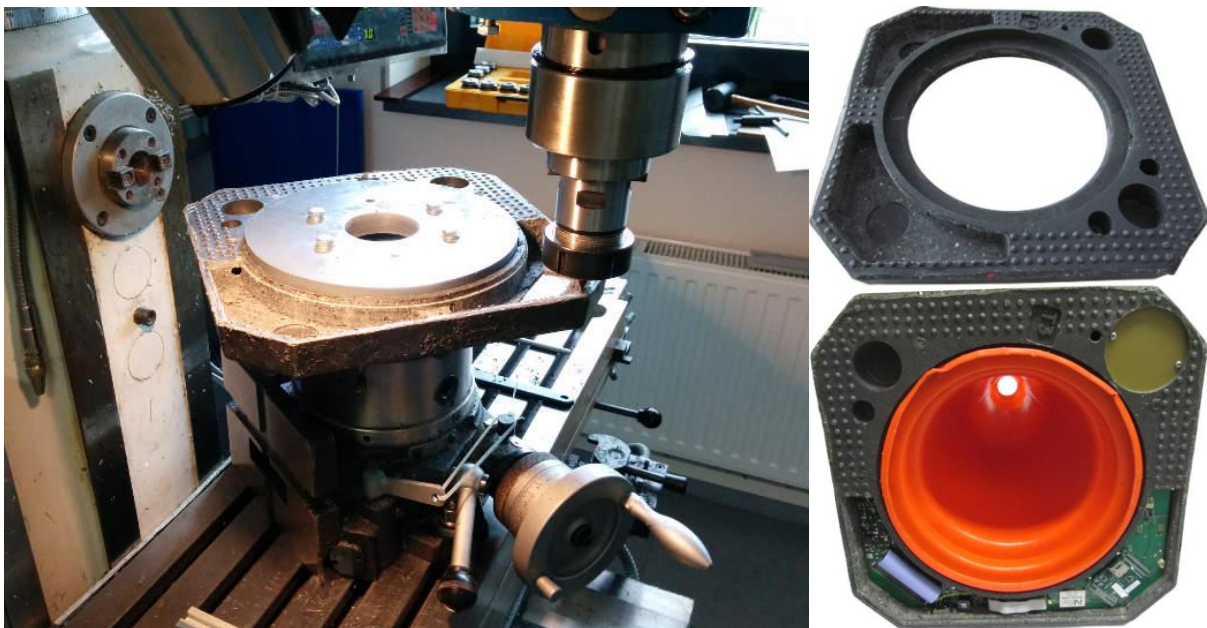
mechanische Fertigung der IL-Prototypen in der Werkstatt des ifak (links - Fräsen der Fußplatte in spezieller Spannvorrichtung, rechts – IL Prototyp, gefräste Fußplatte und IL mit integrierter Elektronik)
